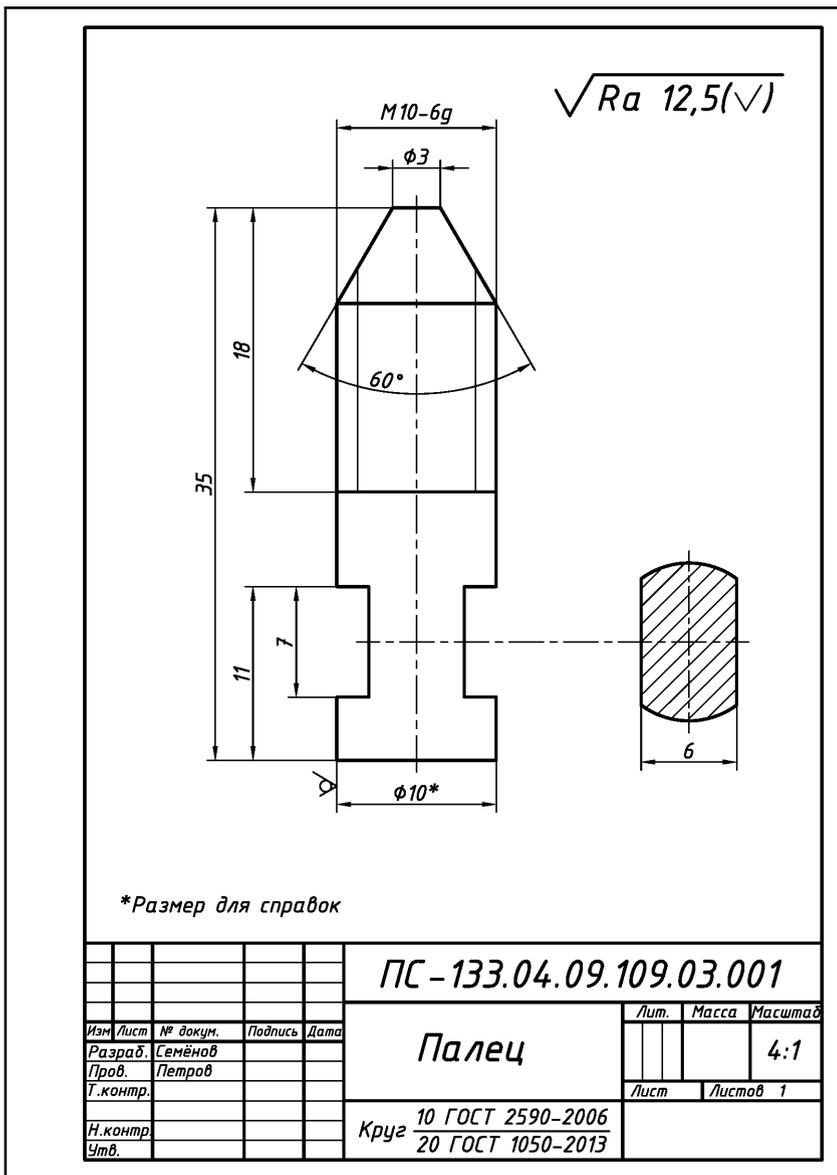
Оформление рабочего чертежа детали «Палец» армированного изделия «Упор» (рис. 1.88)
